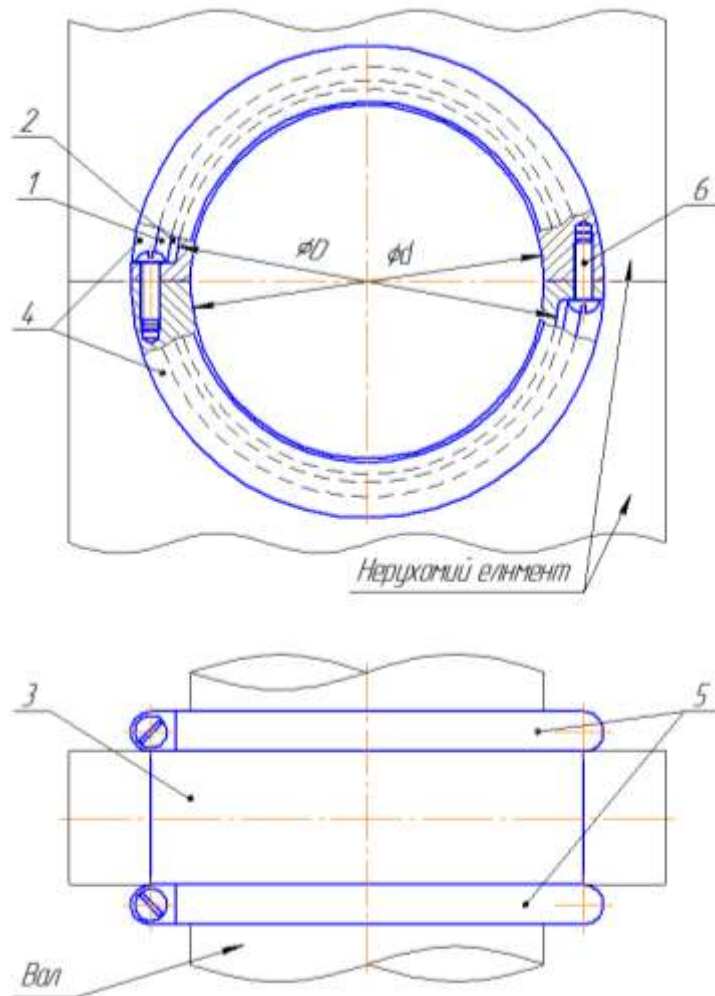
Підшипник ковзання: 1 – напівкільцеві вкладиші пластинчастої форми; 2 – антифрикційний шар, 3 – муфта; 4 – напівмуфта; 5 – реборди; 6 – з'єднувальні гвинти; D – зовнішній діаметр муфти; d – внутрішній діаметр муфти
